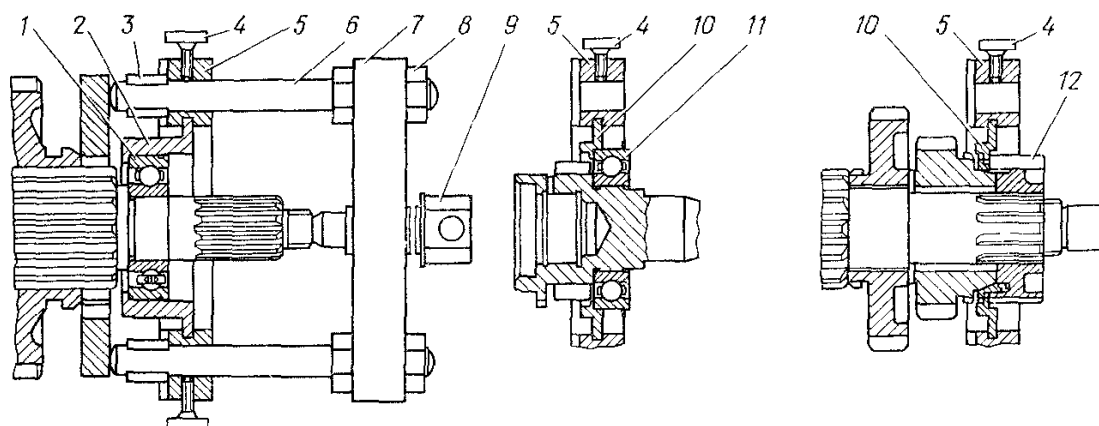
Съемник для снятия ступиц и подшипников с первичного и вторичного валов: 1, 11 — подшипники; 2, 10 — вкладыши; 3 — упор; 4 — винт; 5 — каретка; 6 — шпилька; 7 — граверса; 8 — гайка; 9 — винт; 12 — ступица
